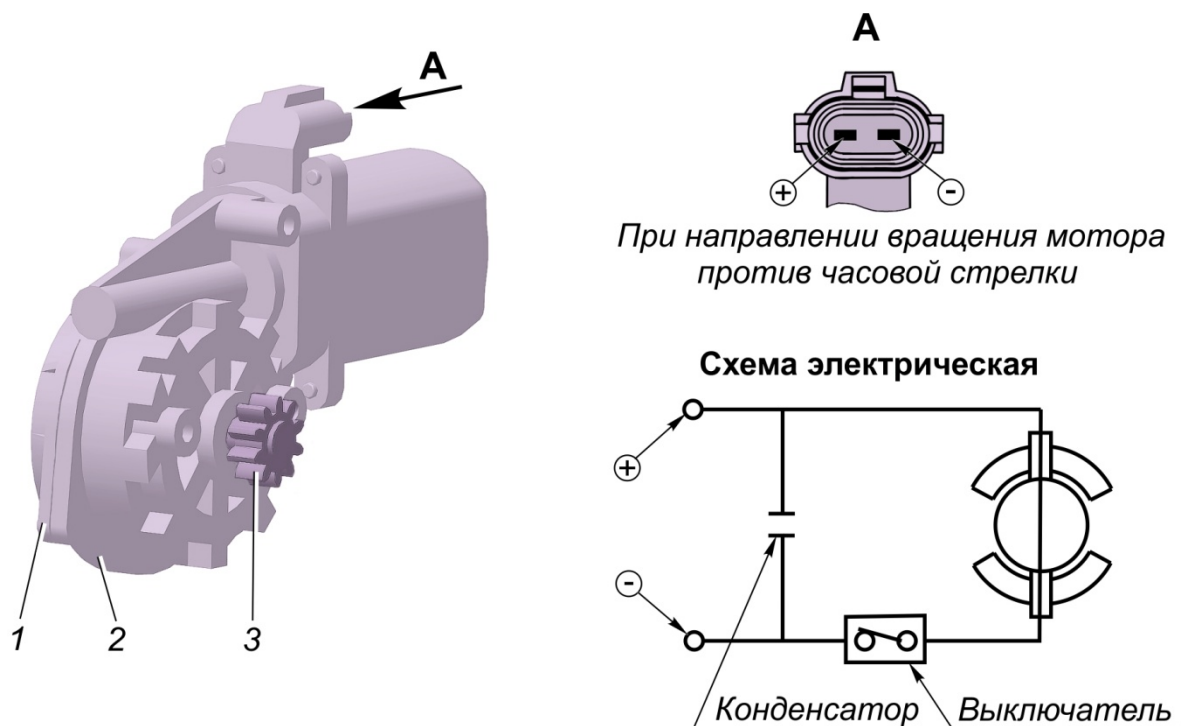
Моторедуктор: 1 – крышка; 2- корпус; 3- ведущая шестерня
